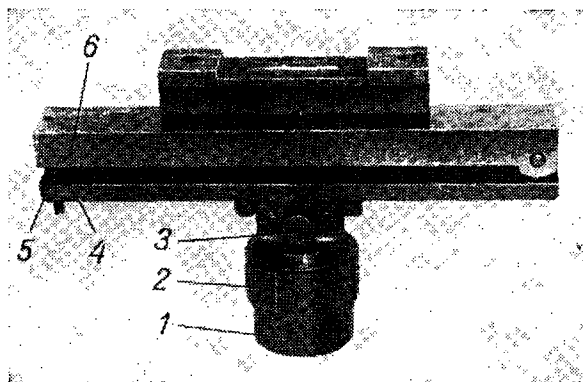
Приспособление для проверки перпендикулярности оси шпинделя направляющим бабки плоскошлифовального станка
